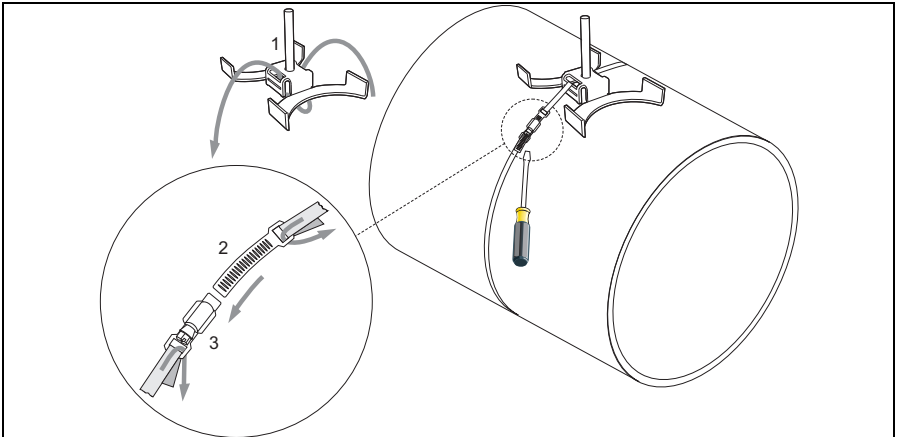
Montaggio preliminare delle fascette di fissaggio per diametri del tubo DN >200 (8")
